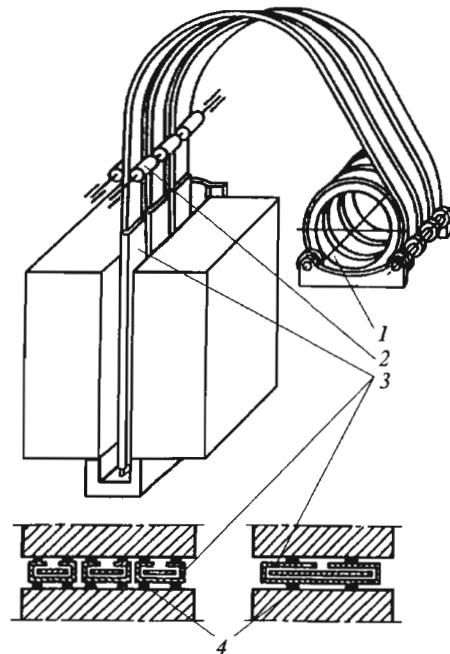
Схема сварки ленточными электродами:
